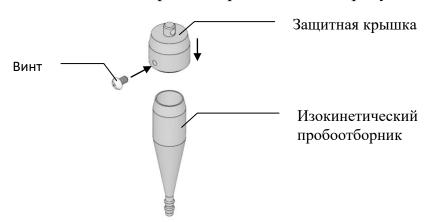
Схема установки защитной крышки на пробоотборник
